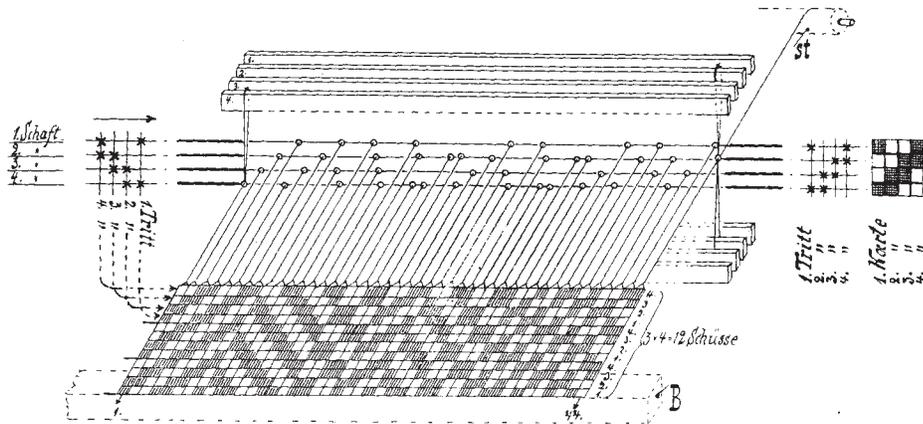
Reduzierter Geschirreinzug und Tritt- oder Kartenzeichnung.
